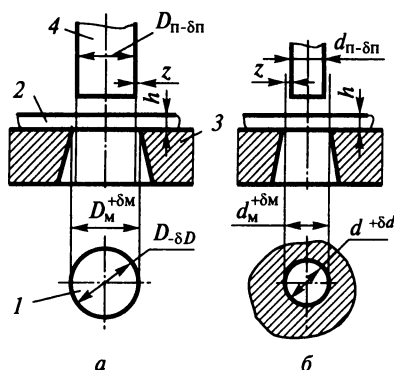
Вырубка детали диаметром D (а) и пробивка отверстия диаметром d (б)
